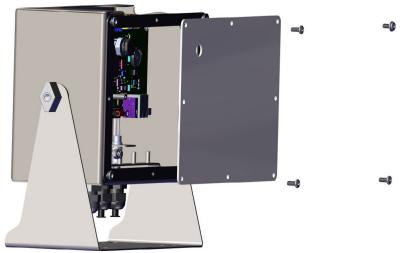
Desmontaje de la placa posterior del alojamiento universal
